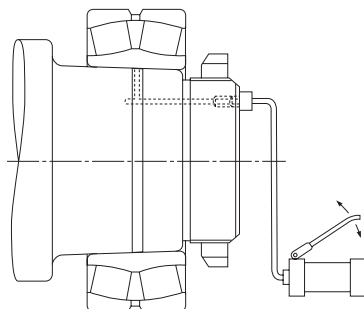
Demontage einer Abziehhülse mit Abziehmutter (1)
